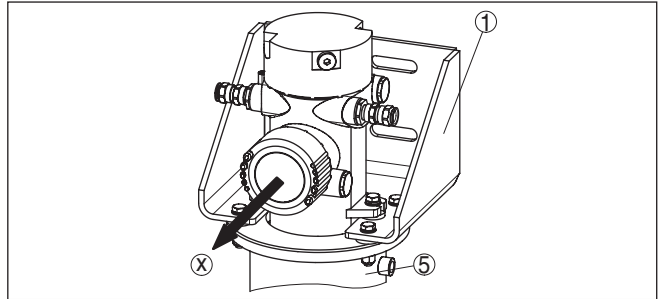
Montagerichting van de sensor ten opzichte van de bevestigingsbeugel
